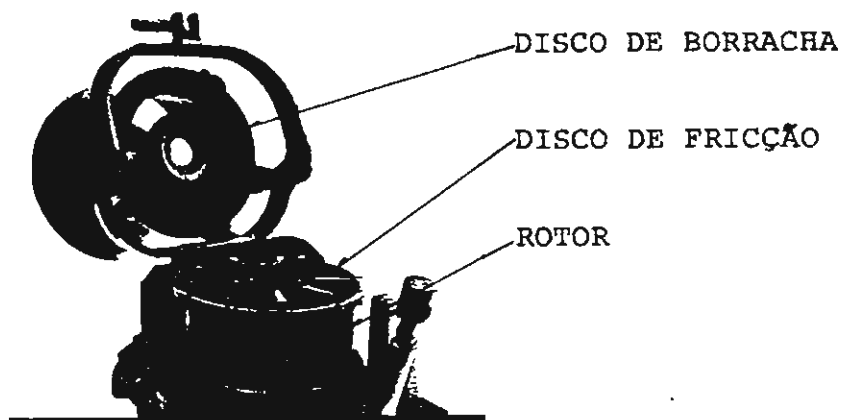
Detalhe de montagem do conjunto rotor de câmaras, discos de fricção e discos de borracha.
